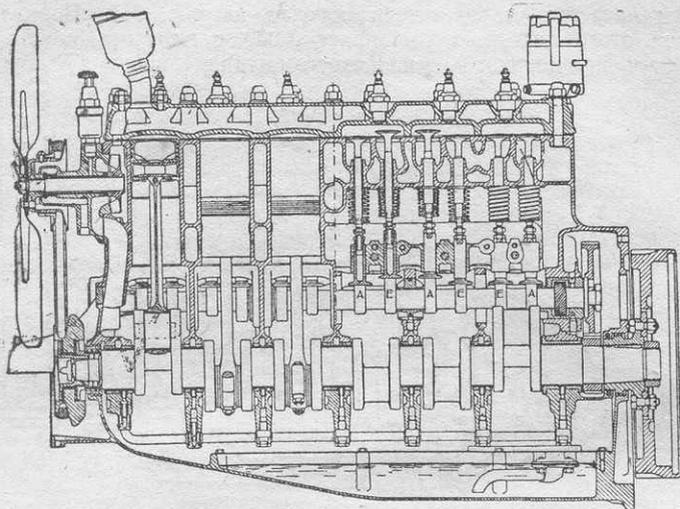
Продольный разрез 2-литрового двигателя «Мерседес-Бенц».
